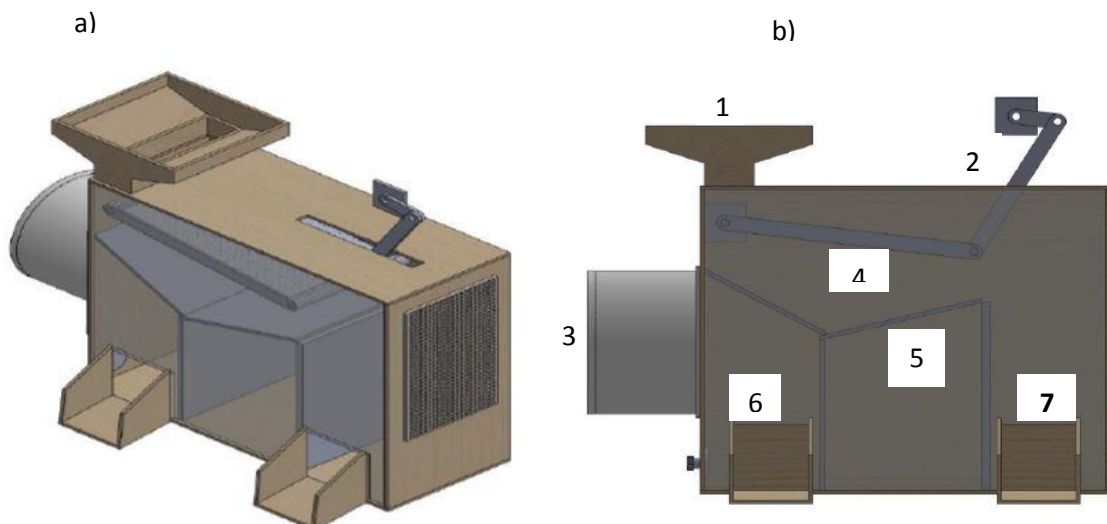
Diseño paramétrico-3D de componentes del mecanismo de la máquina
